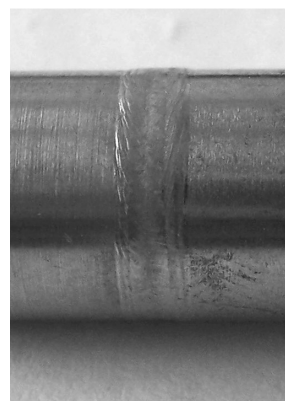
Внешний вид сварного соединения из сталей STS 410 JIS S45C
